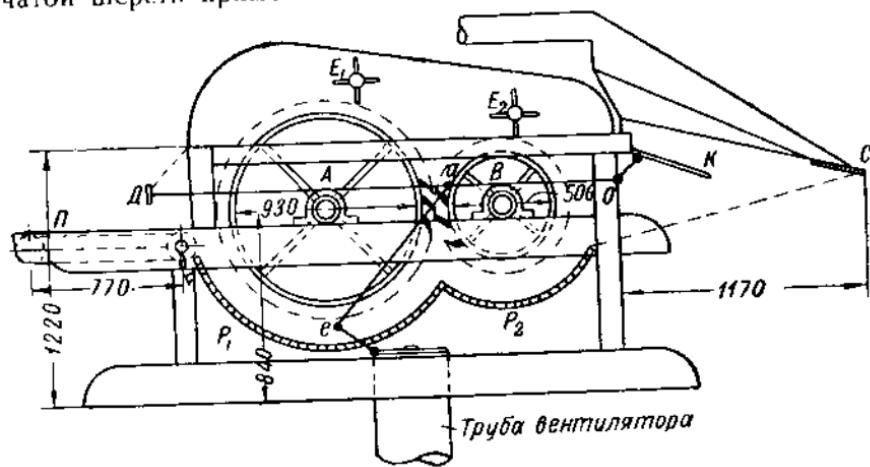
Машина для разрыхления и очистки свальчатой шерсти
